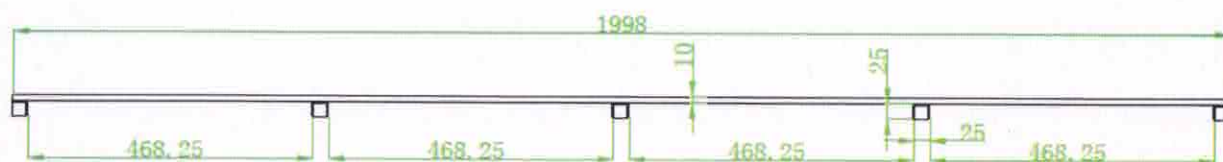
Vista lateral do estrado (medidas em milímetros)
